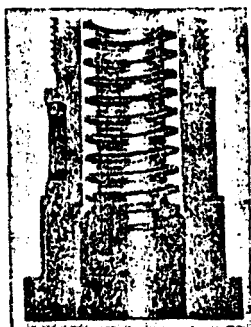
Биметаллические детали нефтяного оборудования, изготовленные наплавкой трением
